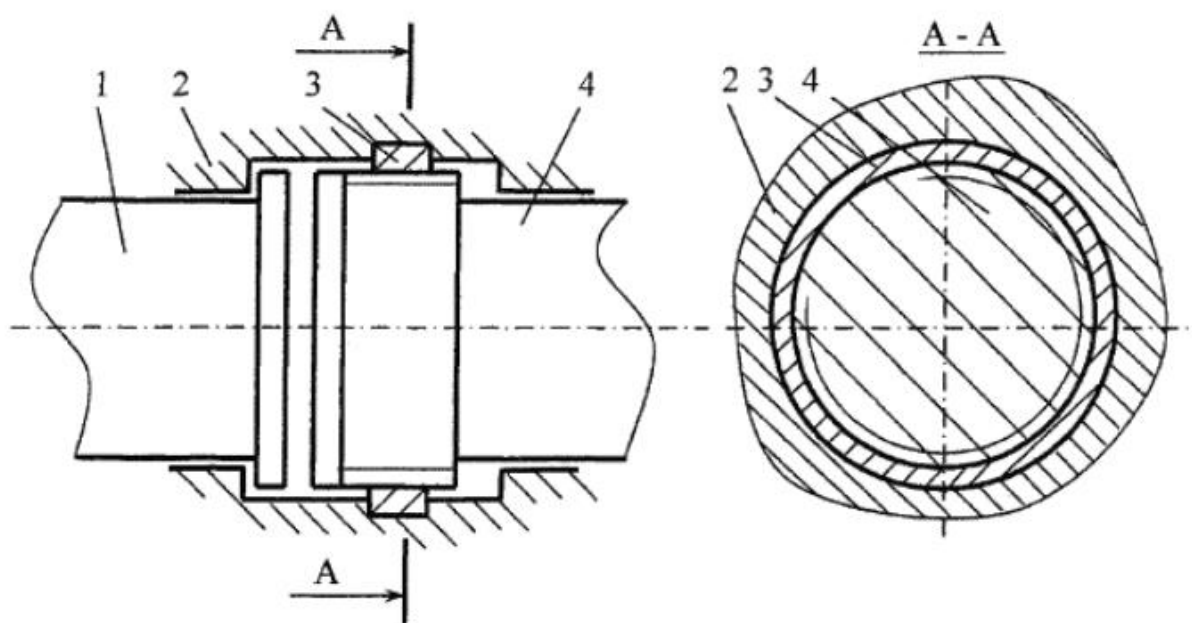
Схема механизма свободного хода с торцевой фрикционной поверхностью
